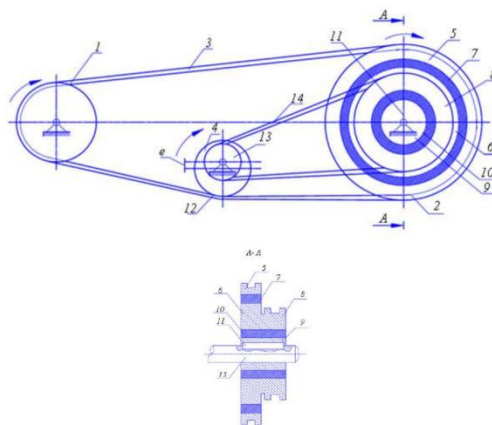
Схема ременная передача, стабилизирующая движение ведущего шкива
